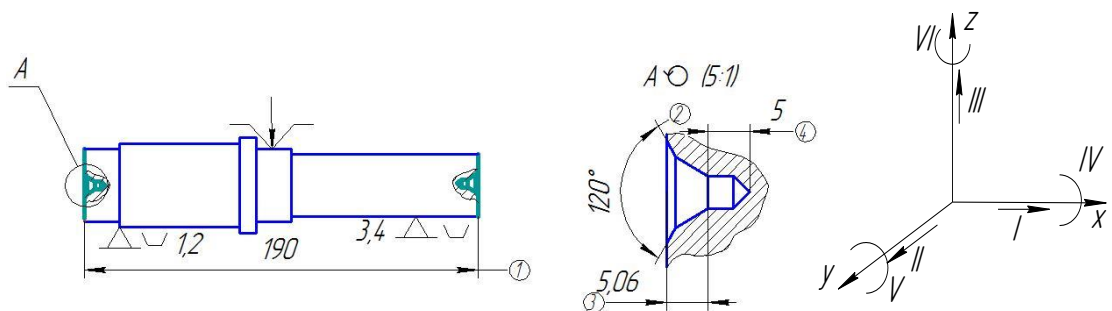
Схема базування заготовки на фрезерно-центрувальній операції
